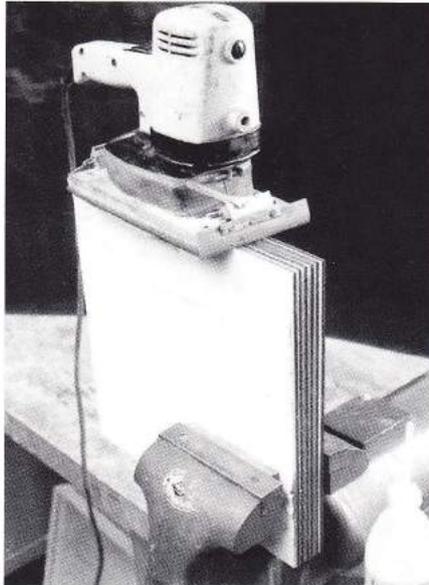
Шлифование торца стопки заготовок при помощи орбитального шлифовального станка
